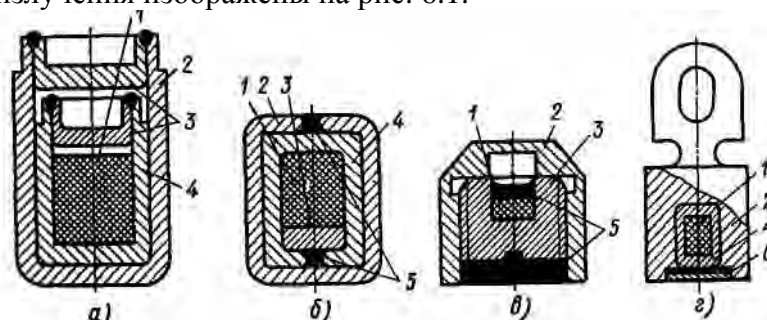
Виды радиоизотопных источников с разной герметизацией: а — сваркой или пайкой; б — завальцовкой и клейкой; в — на резьбз с заливкой; г — завальцовка и заливка (1 — радиоактивное вещество, 2 — защитный корпус, 3 — крышка, 4 — внутренняя оболочка ампулы; 5 — герметик, 6 — мишень)
